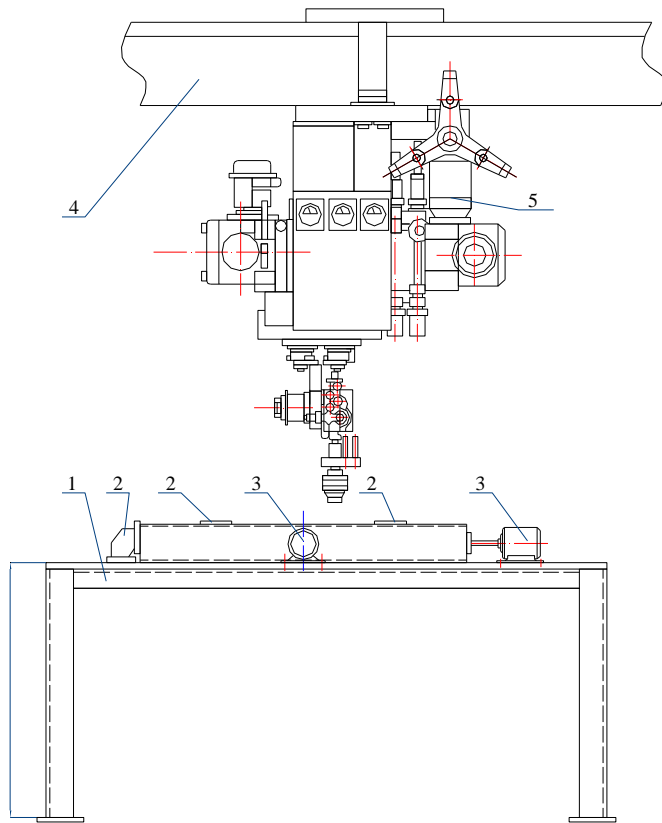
Кондуктор для сборки и сварки балок рамы.
